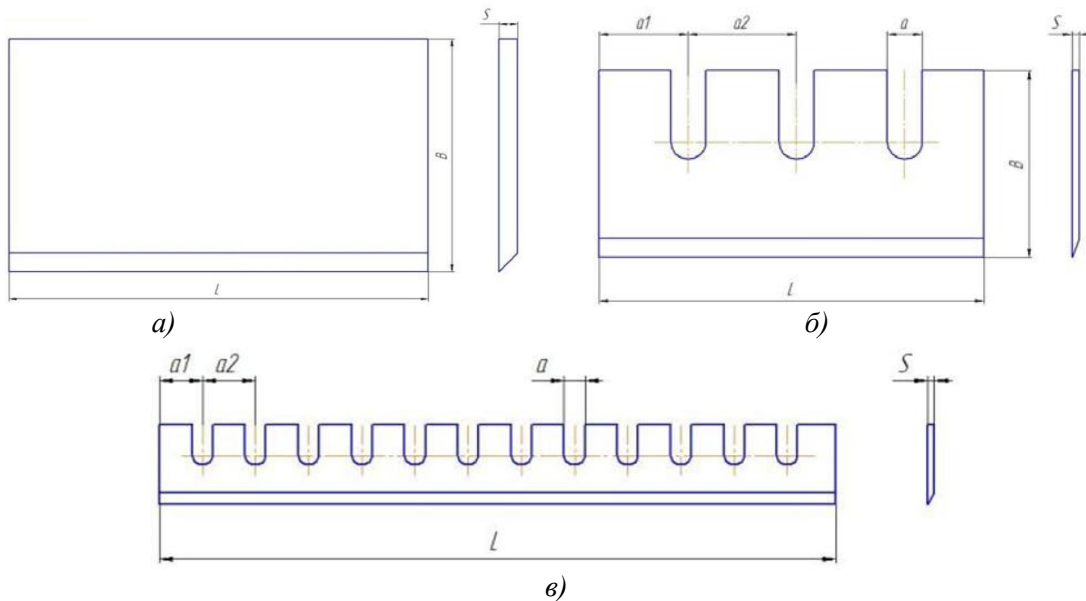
Креслення різних за конфігурацією деревообробних ножів: а – ніж гільйотинних ножниць для різання шпону; б – ніж для дрібної порізки деревини в сірниковій промисловості; в – ніж для фрезерування деревини з прямолінійною кромкою
